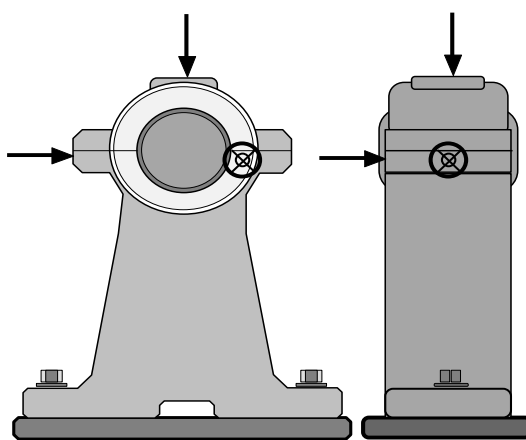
Типичные контрольные точки измерений вибрации на корпусе подшипника.
